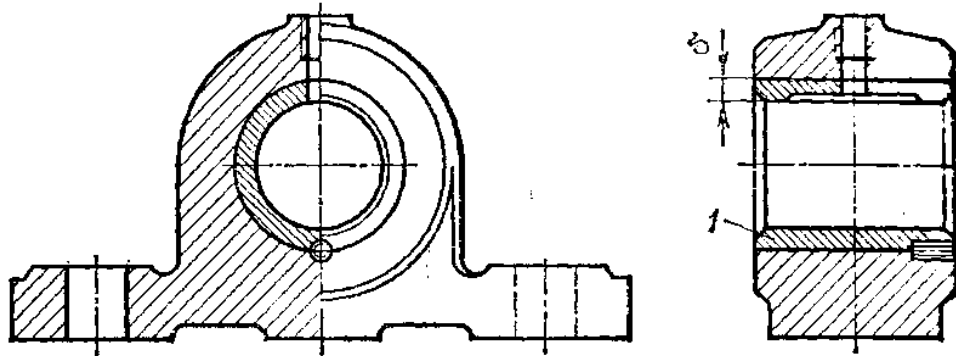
Конструкція нероз’ємного підшипника ковзання
